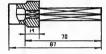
Приспособление для отворачивания пробки в блоке цилиндров «Москвича-412».
